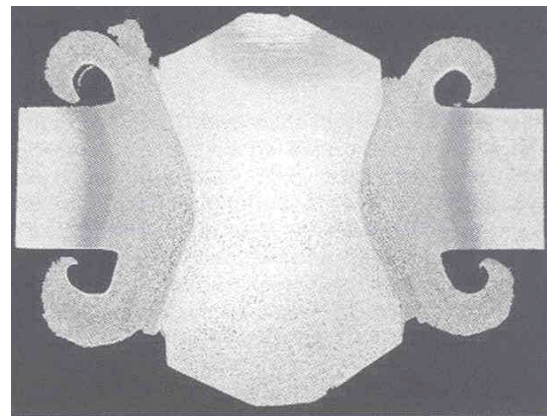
Schweißung eines X42 Rohres (Rohrdurchmesser: 114mm)
